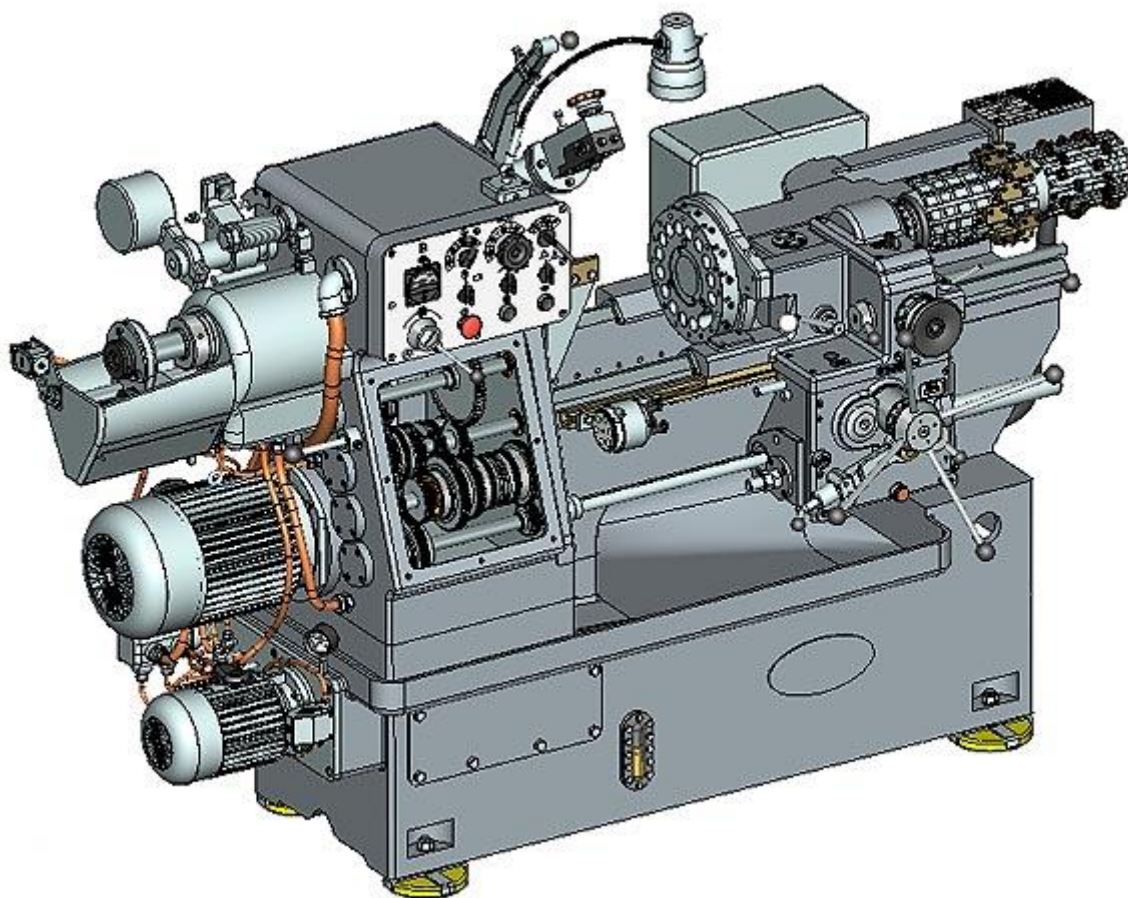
Токарно-револьверний верстат моделі 1341
